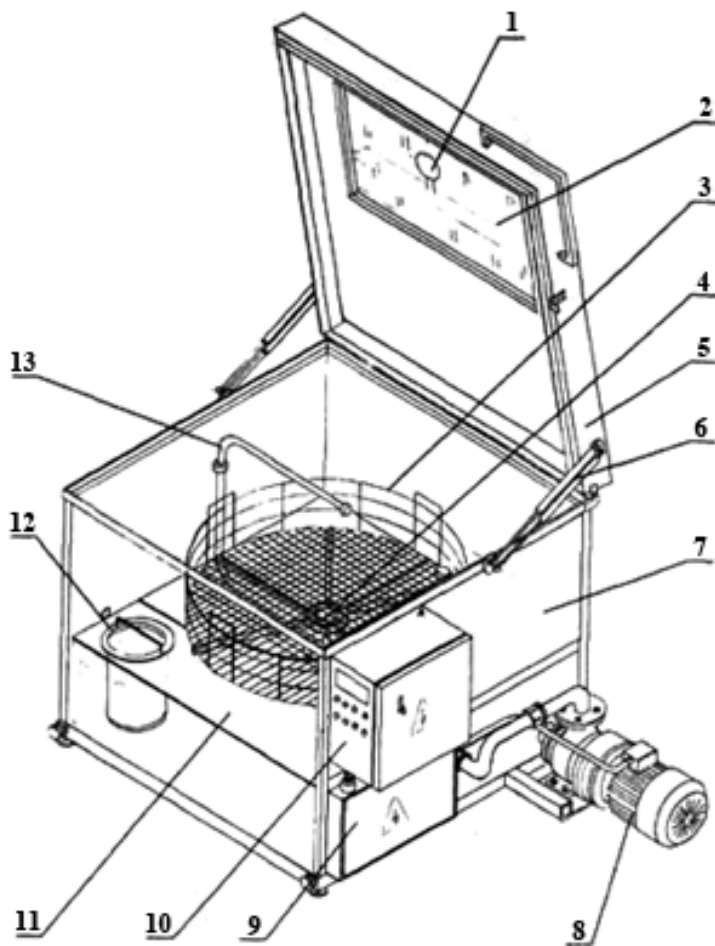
Схема установки моечной стационарной ОМ-35455М: 1 – люк; 2 – окно; 3 – корзина; 4 – стол моечный; 5 – крышка откидная; 6 – пружинный упор; 7 – камера моечная; 8 – насос; 9 – блок нагрева; 10 – электрошкаф; 11 – металлический лист; 12 – фильтр; 13 – ротор
